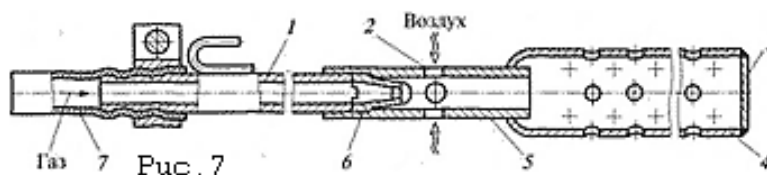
Газовая запальная горелка конструкции Мосгазпроекта: 1-штуцер-удлинитель для присоединения шланга; 2-отверстия для прохода воздуха; 3-торцевая пластинка; 4-огневой насадок; 5-воздушная обойма; 6-сопло; 7-гибкий шланг.
